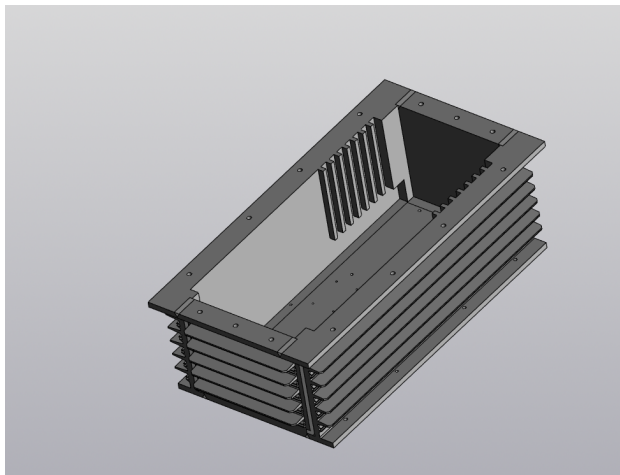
Внешний вид корпуса после сваривания швеллеров и основания
